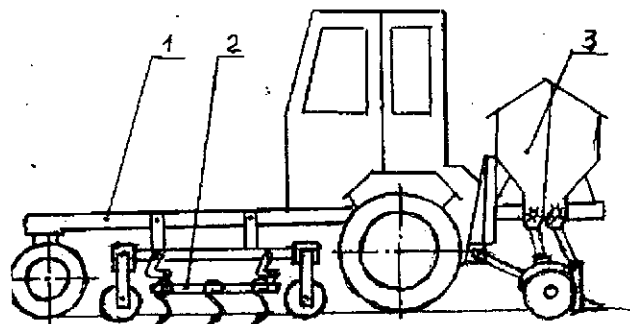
Схема почвообрабатывающего посевного агрегата:
